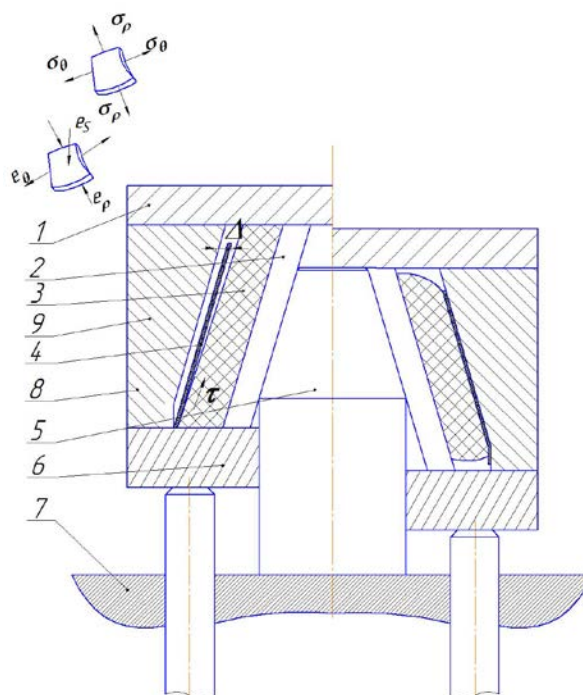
Способ формообразования тонкостенных осесимметричных деталей усеченной сужающейся формы на основе процесса отбортовки: 1 - верхняя плита штампа; 2 - раздвижные сектора; 3 - эластичный элемент; 4 - заготовка; 5 - конус; 6 - опорное кольцо; 7 - нижняя плита штампа; 8 - матрица; 9 - деталь
